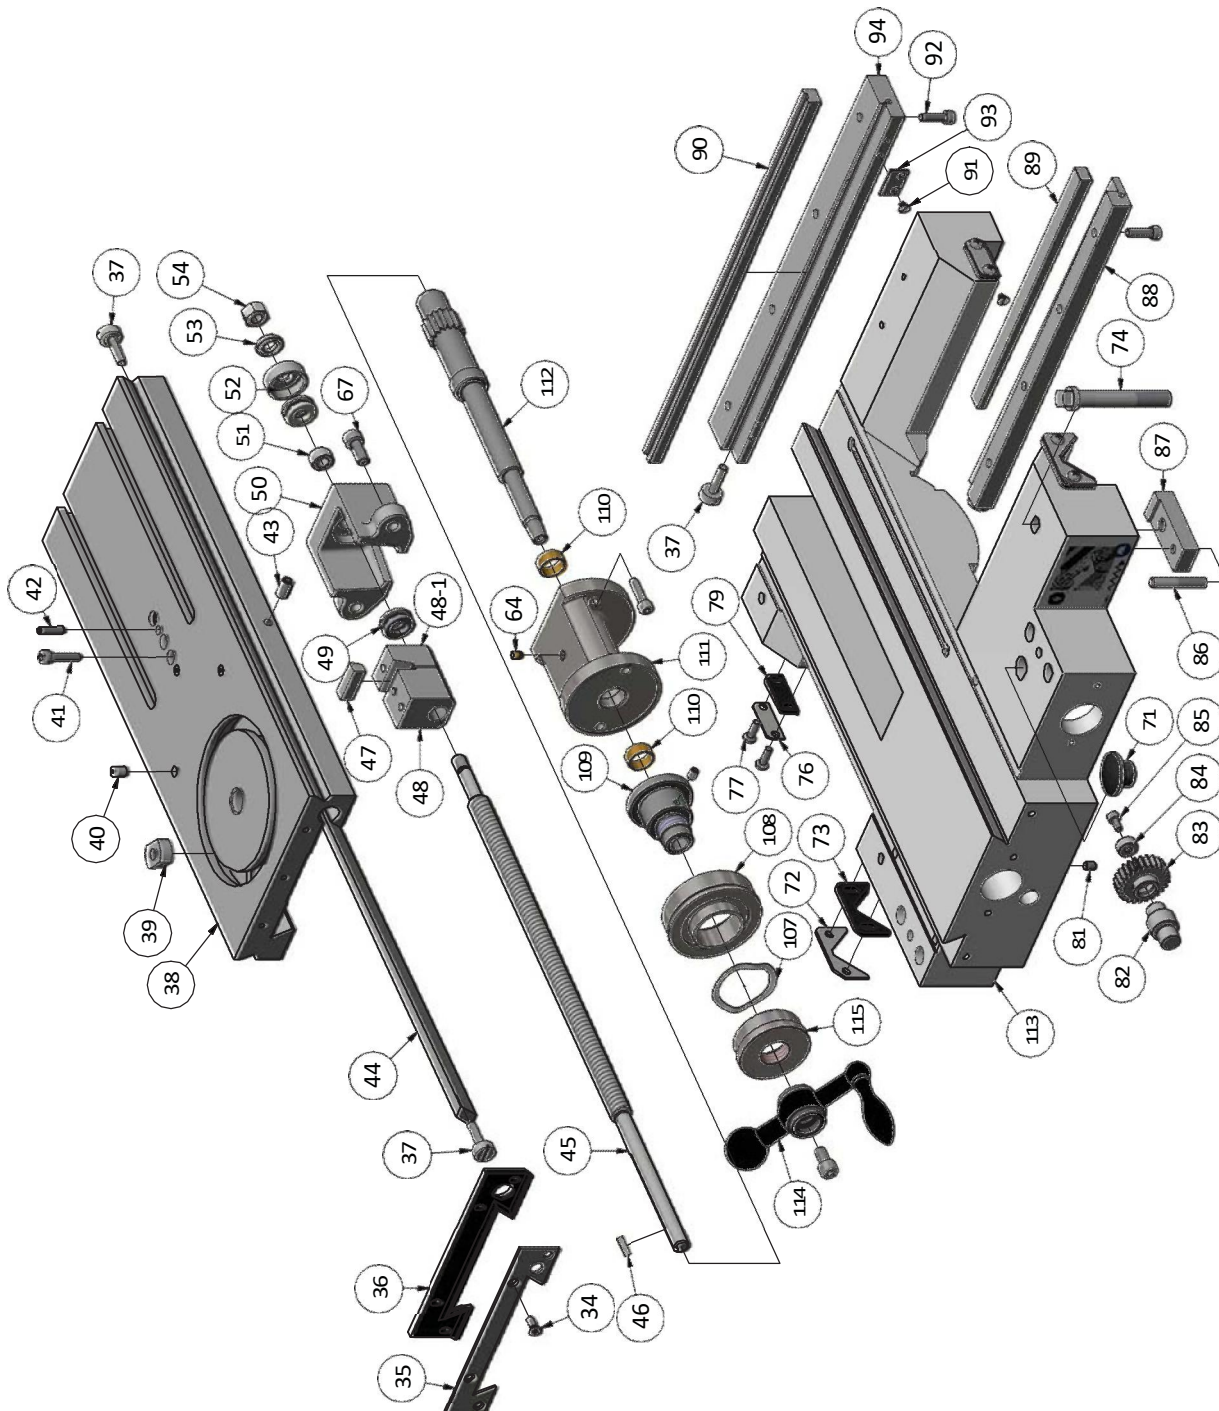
Planschlitten 2-2 – Carro compuesto 2-2
